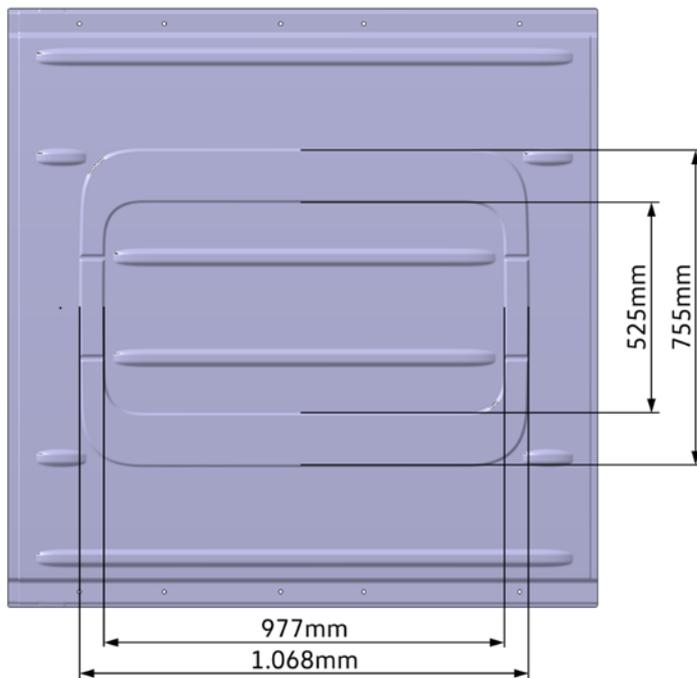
Dimensions des surfaces estampées sur le pavillon surélevé
